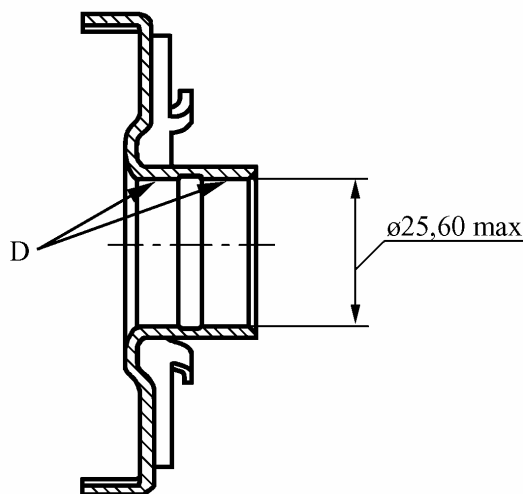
Муфта 2110-1601181 подшипника выключения сцепления:
